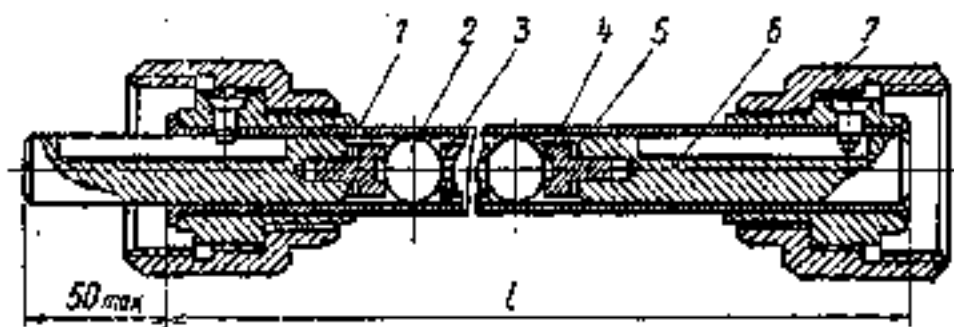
Конструкция шарикового передаточного механизма (ШПМ):
